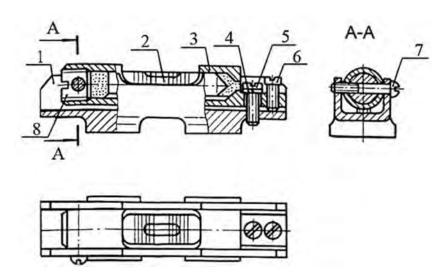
Контрольный уровень: I — литой или сварной корпус; 2 — ампула в оправе; 3 — трубка; 4 — шайба; 5, 6, 7 — винты; 8 — пробка
